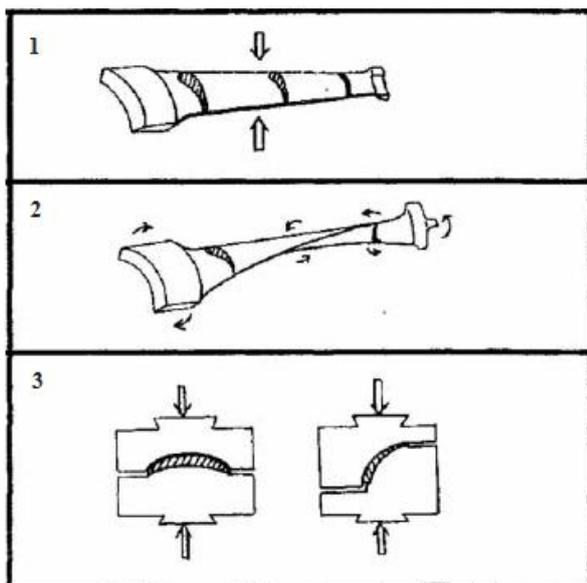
Трехступенчатый процесс штамповки лопатки: 1 – расплющивание; 2 – скручивание; 3 – окончательная штамповка
